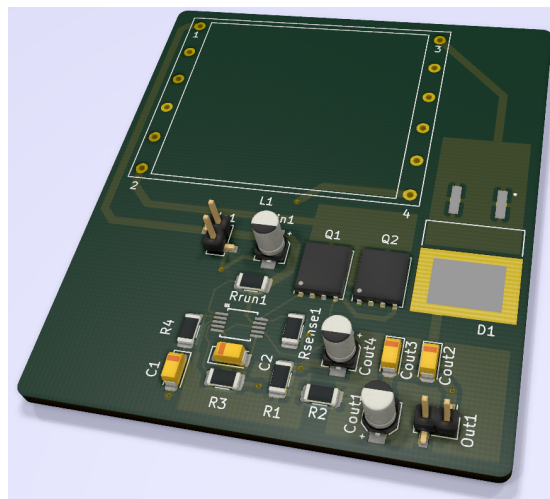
Modelo en tres dimensiones del PCB diseñado.
